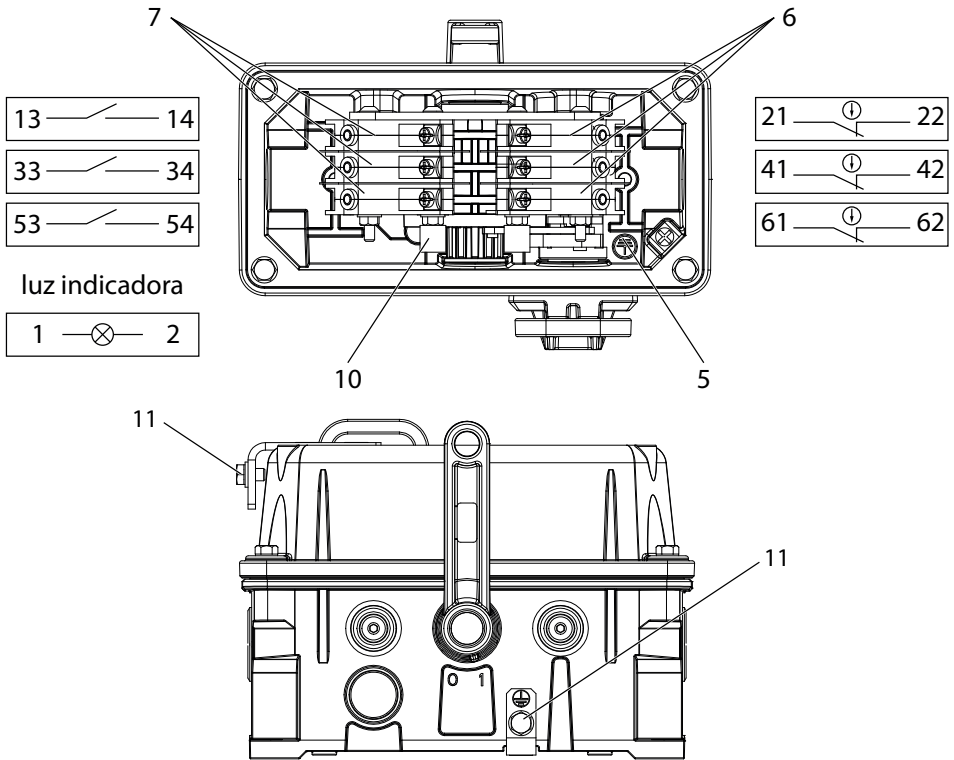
Conexión eléctrica (interruptor con equipamiento máximo, conexión de puesta a tierra y luz indicadora)
